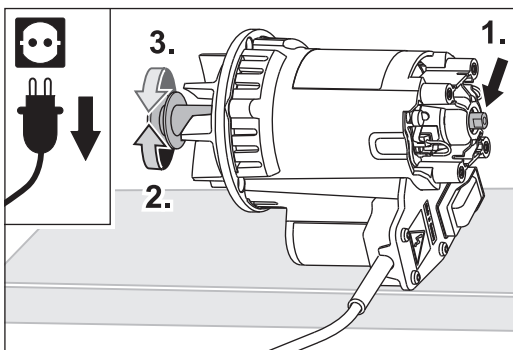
Håll fast motoraxelns ände med en skruvnyckel (1.) och skruva av motorremskivan från axeln (2.). Skruva på den nya motorremskivan (3.)
